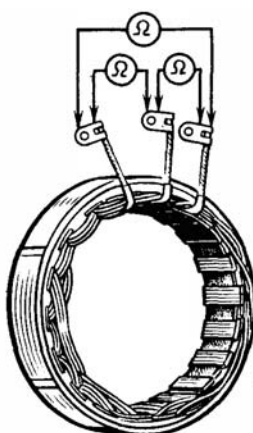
Схема проверки статора генератора на обрыв
